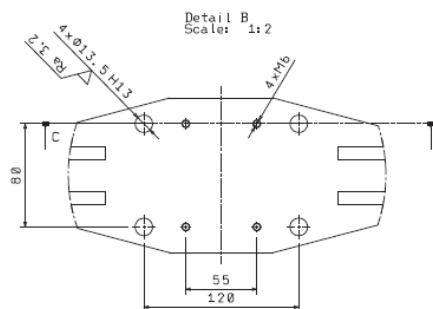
Detail přebrobení otvorů pro měření kolových sil.
